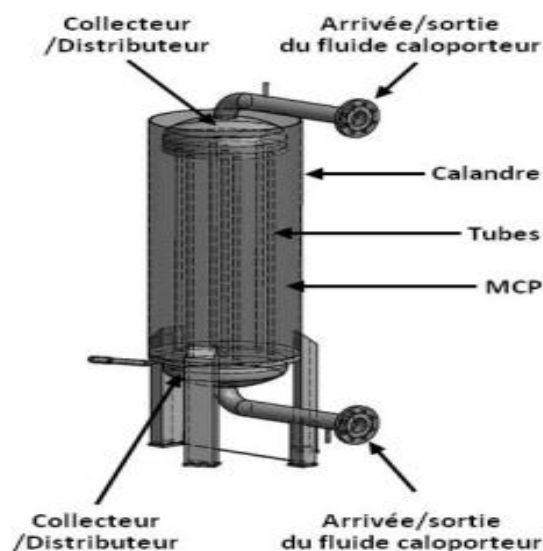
Exemple de système de stockage de type tubes & calandre.
